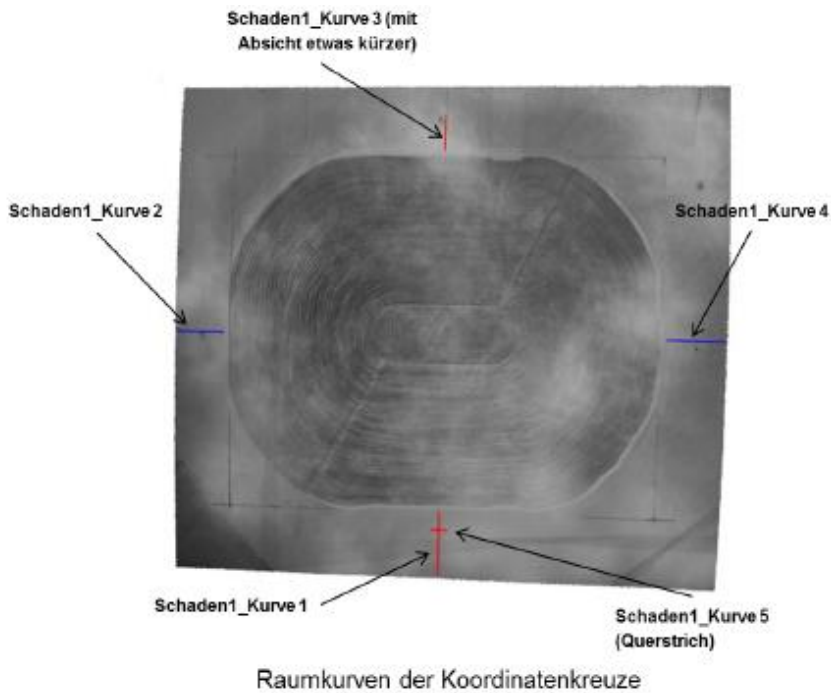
ATOS San-Datenaufbereitung Schaden 1 für Werkzeugfräsen
